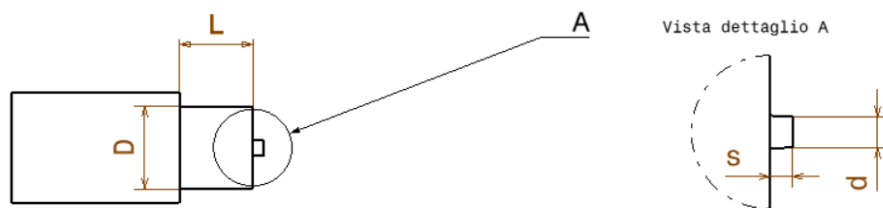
Disegno tecnico di un utensile di FSW con in evidenza i principali parametri geometrici^[5]
